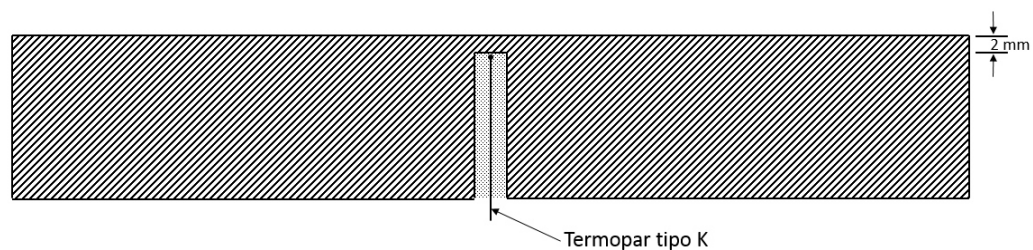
Posición del termopar dentro de la pieza de aluminio.
